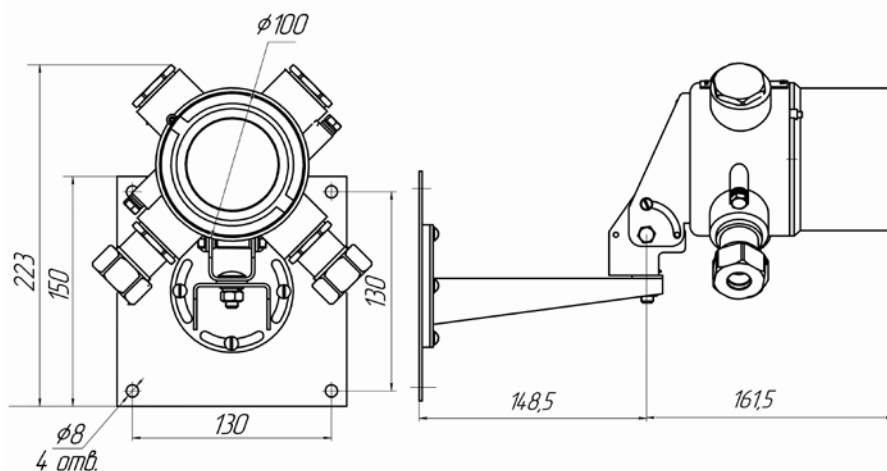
Габаритные и присоединительные размеры датчика движения ВЭЛАН-SENSOR-MOVE
